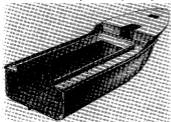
Общий вид конструкции корпуса и палубы грузового теплохода.
